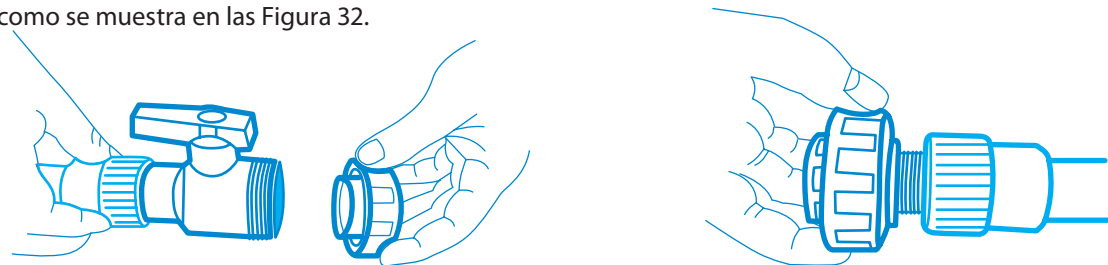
Conexión de tuerca de Válvula General a conector macho de ensamble de Bomba.
